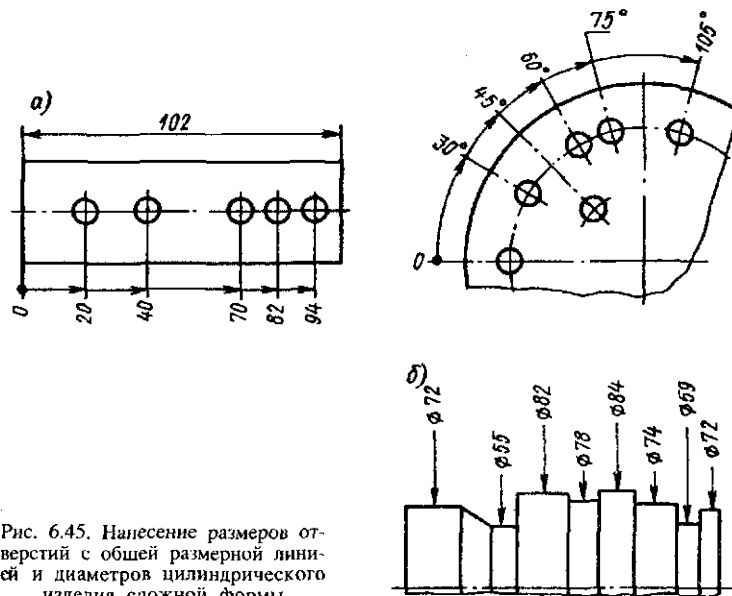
Нанесение размеров отверстий с общей размерной линией и диаметров цилиндрического изделия сложной формы
